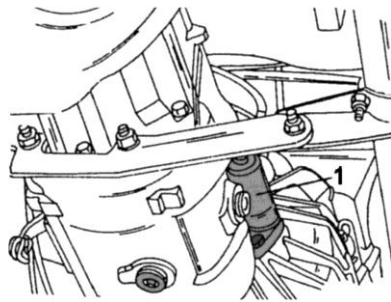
Розташування робочого циліндра (1) зчеплення
